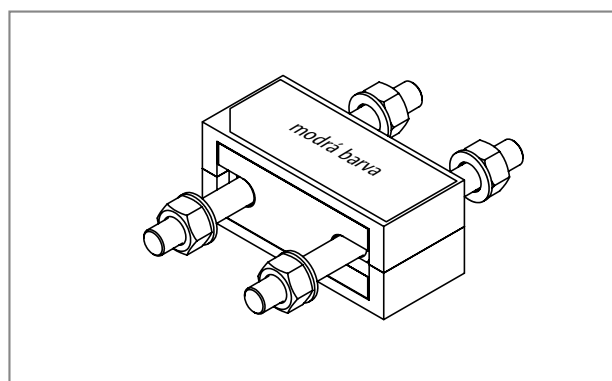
Schöck Isokorb® T typ S-V-D16: Pohled
